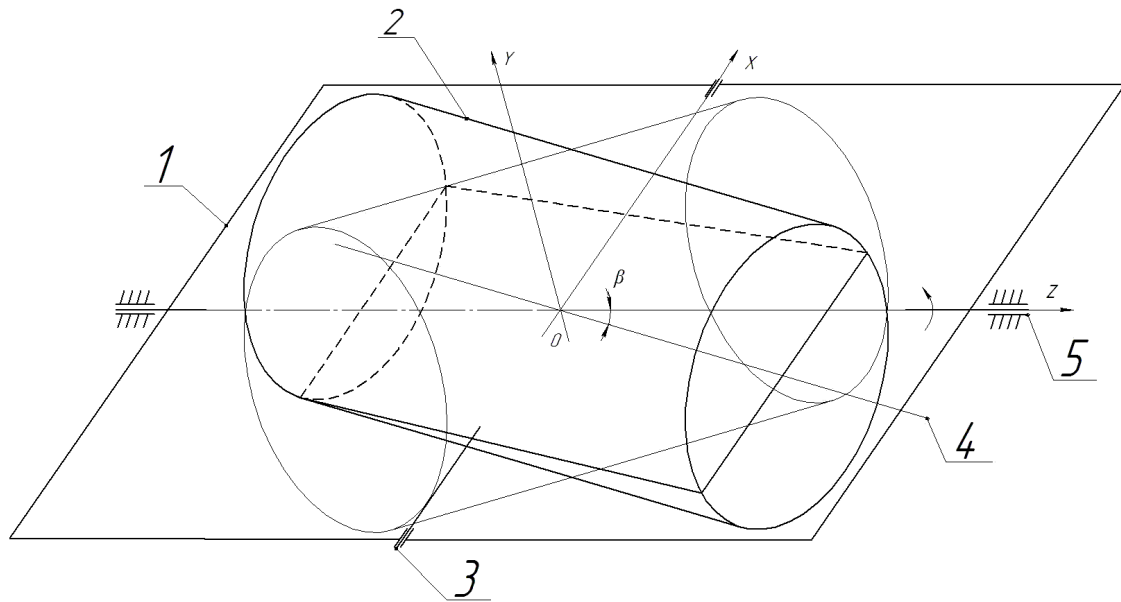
Схема барабанного змішувача: 1 – обертова рама барабанного змішувача; 2 – барабан; 3 – регулятор кута нахилу барабана; 4 – вісь барабана; 5 – вісь обертання рами барабанного змішувача.
